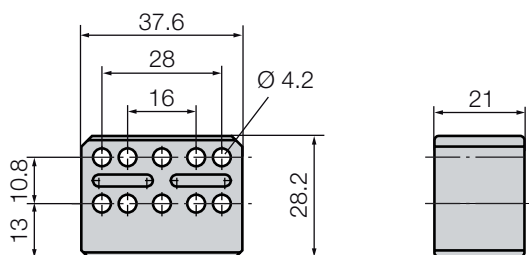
Medidas de montaje de los sensores de posición BTL6-A-3800-2
